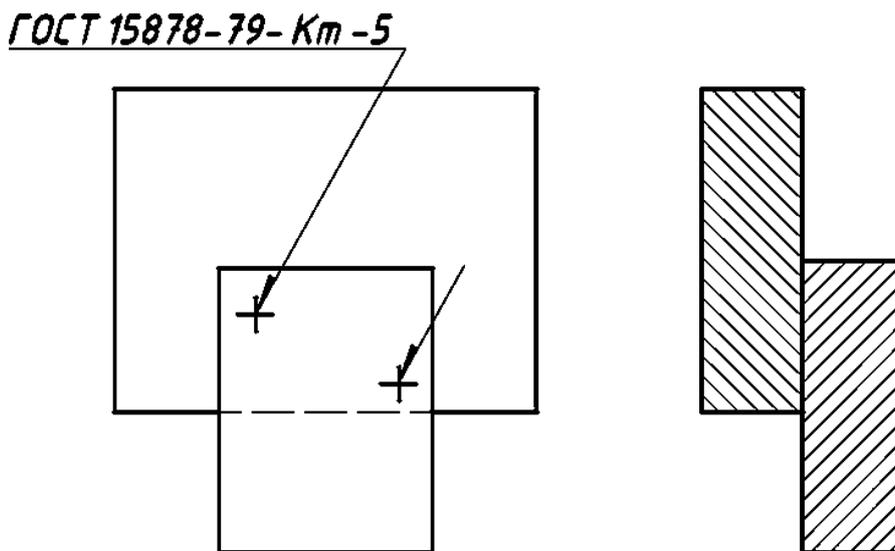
Образец условного обозначения одиночной сварной точки
